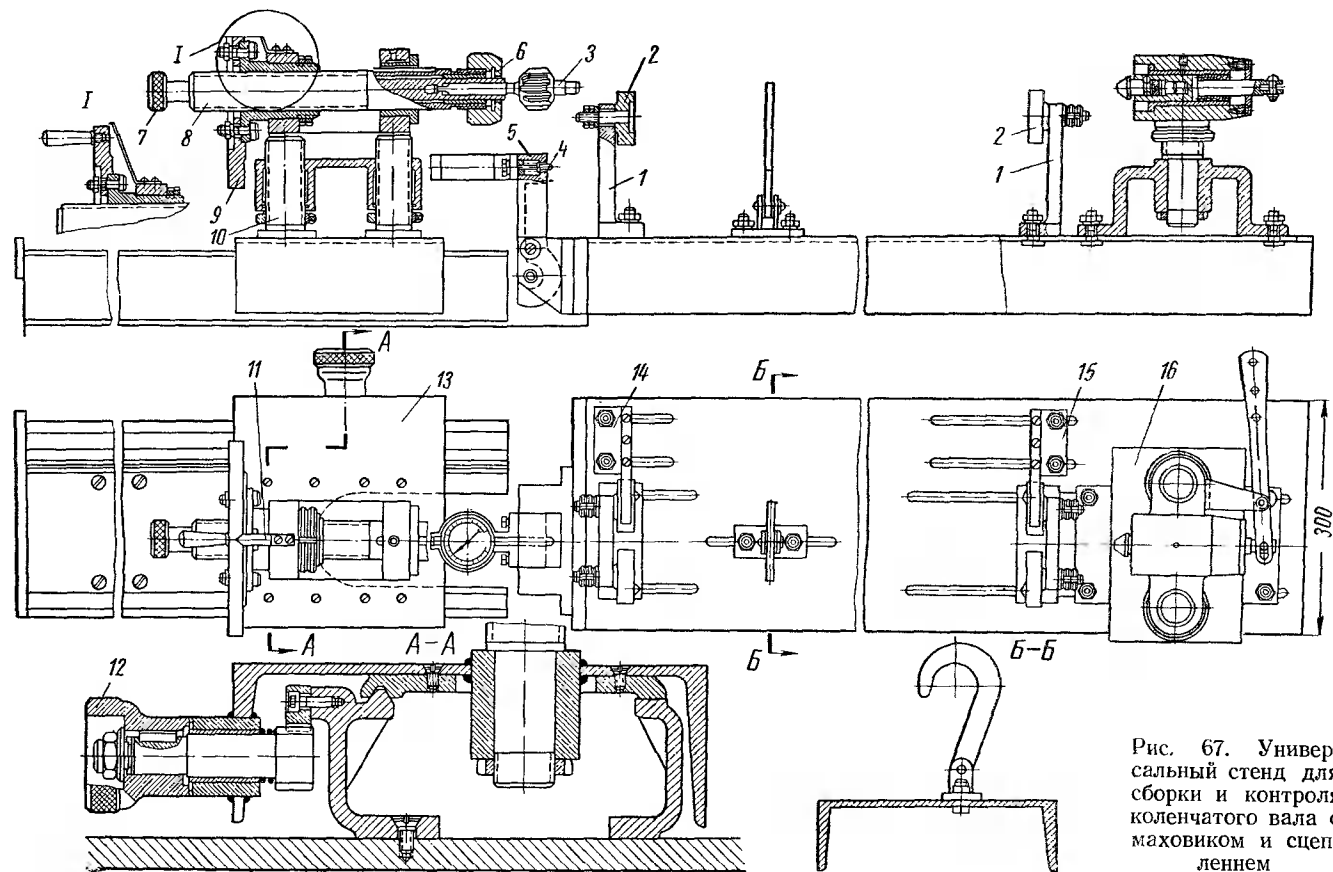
Универсальный стенд для сборки и контроля коленчатого вала с маховиком и сцеплением
